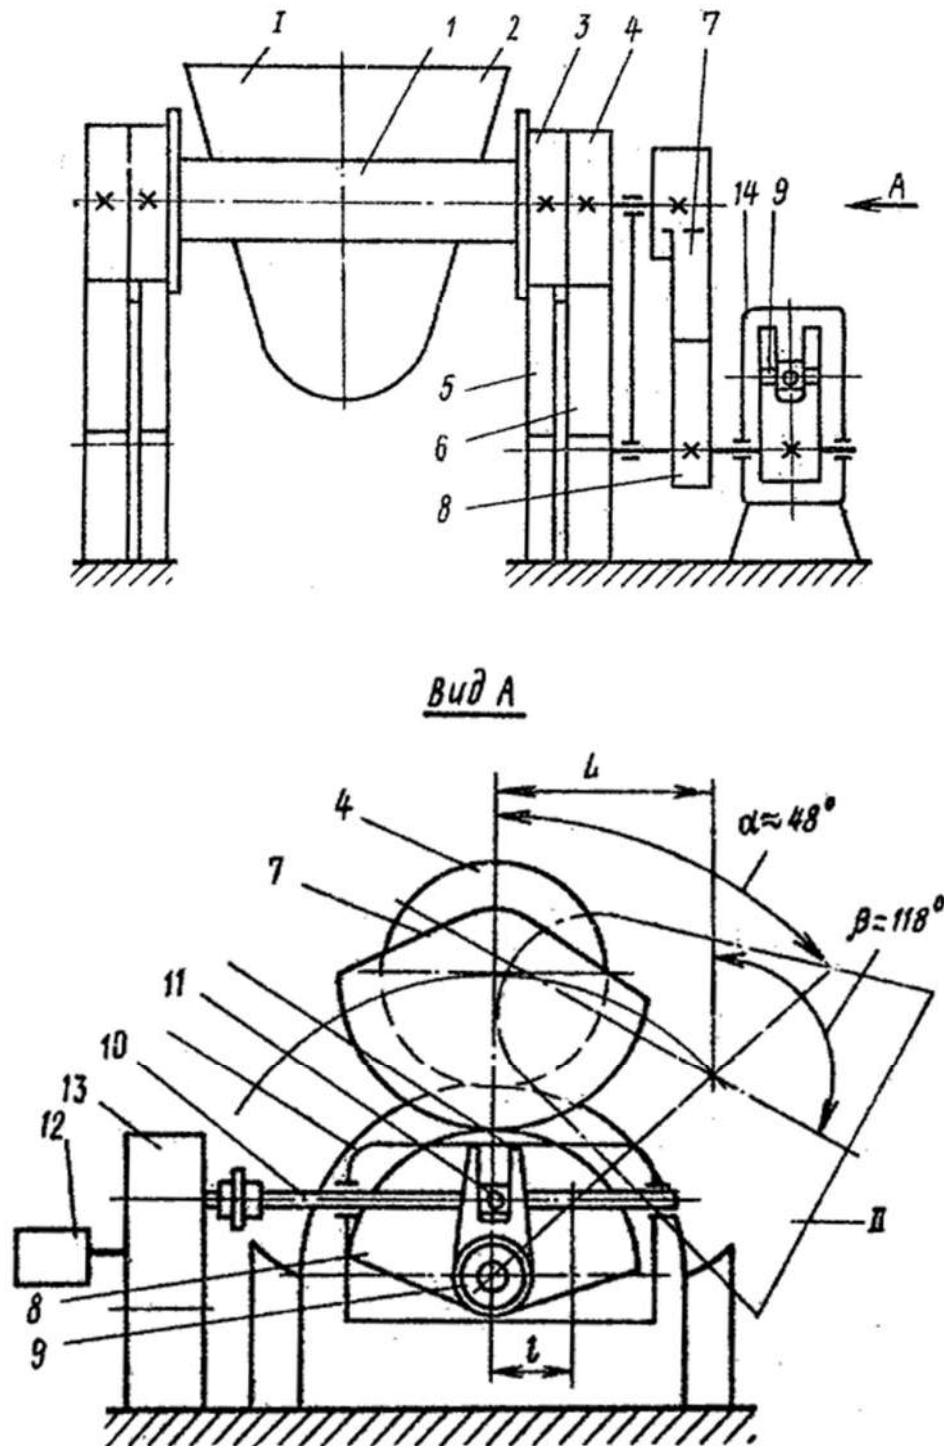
Конструкція механізму кантування чаші шлаковоза
